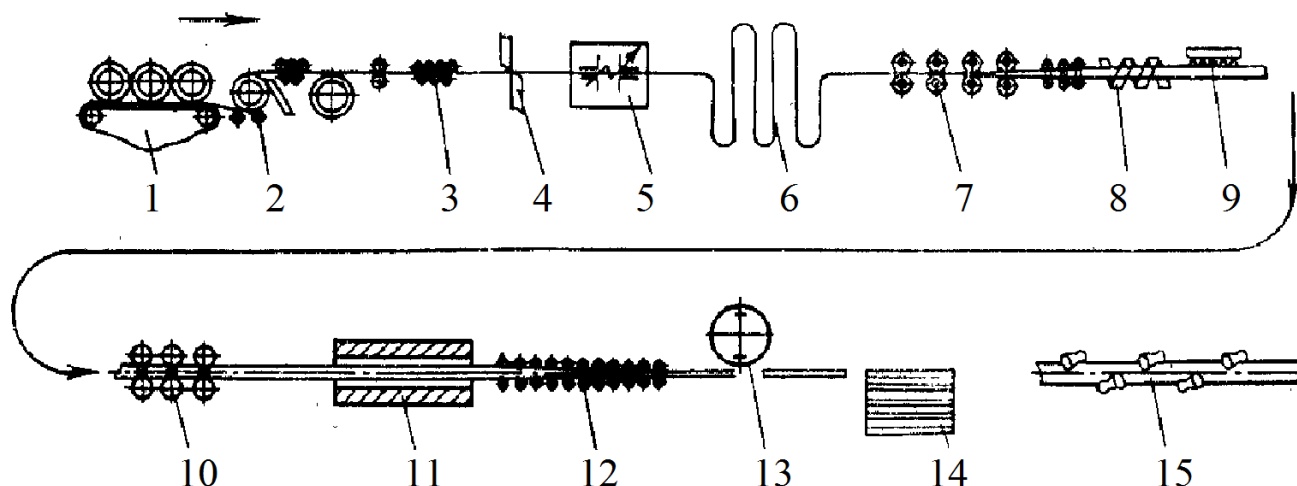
Принципова схема агрегату для високочастотної зварки прямошовних труб
